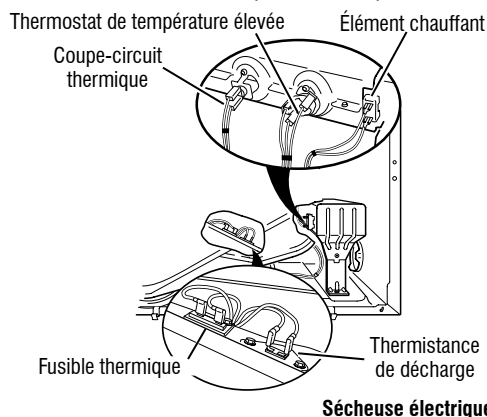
Composants thermiques, sècheuse électrique, vue de face.
